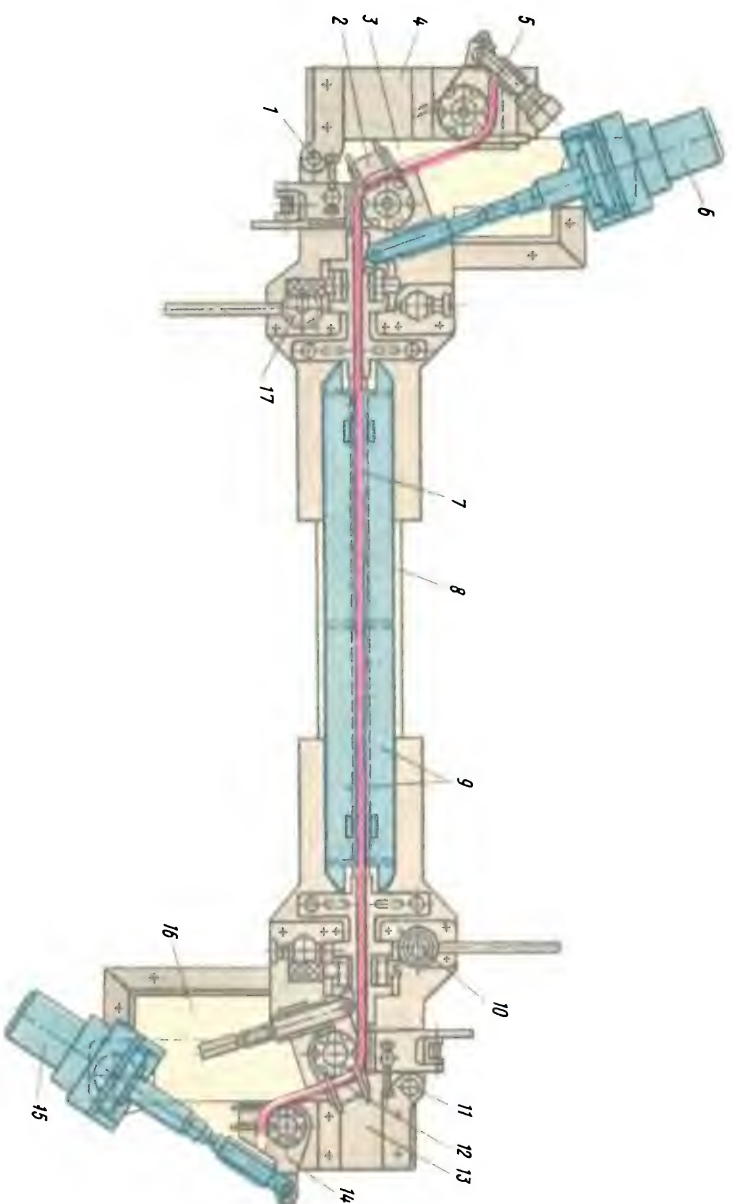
Приспособление для гибки и формовки стержней гидрогенераторов
